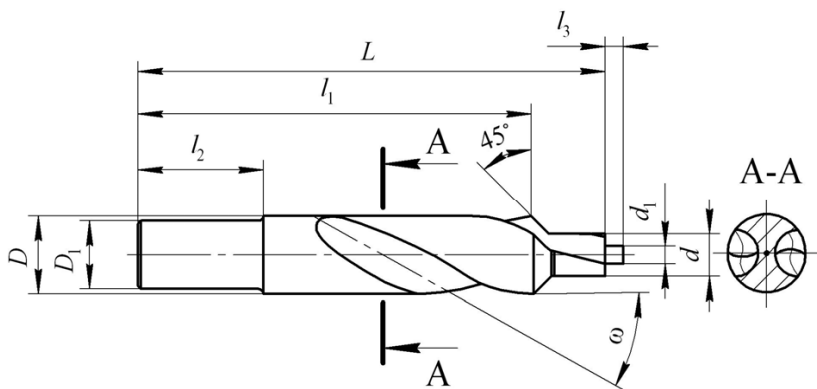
Конструкция твердосплавной заготовки ступенчатого сверла
